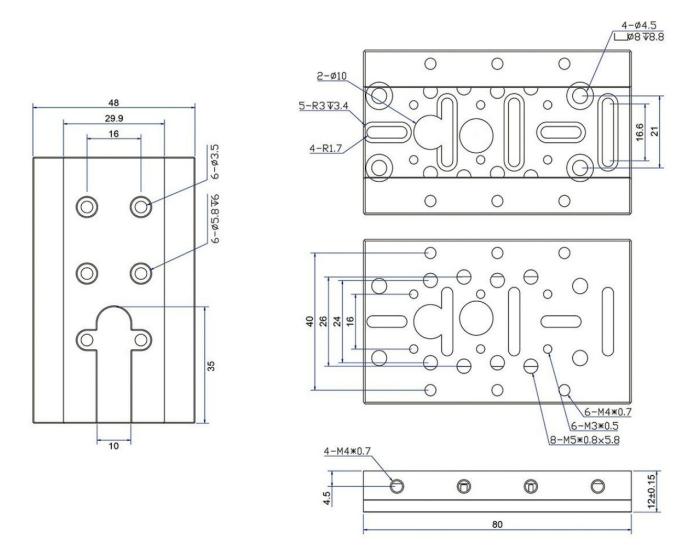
Габаритные и присоединительные размеры монтажной пластины.
